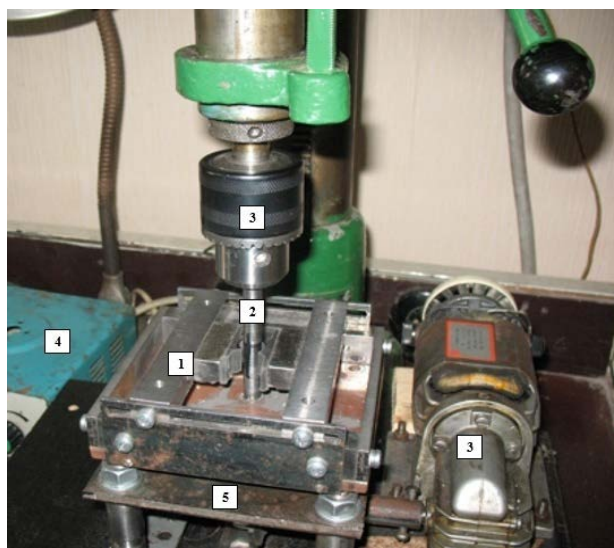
Лабораторная установка для магнитно-абразивной обработки цилиндрических образцов
